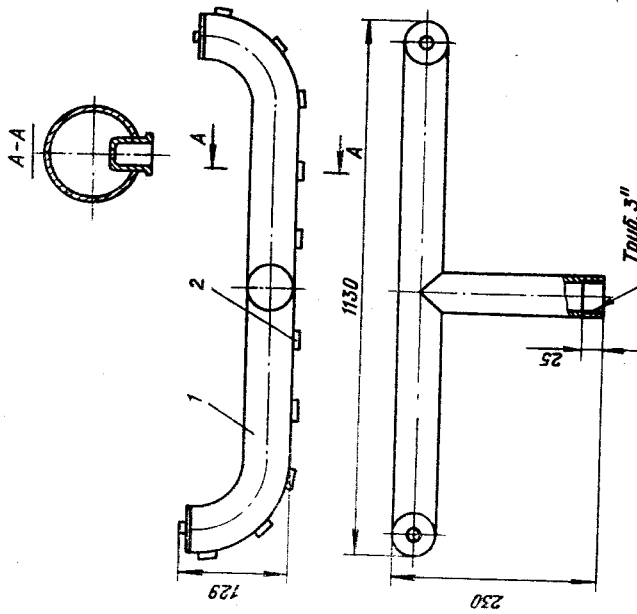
Насадок дуговой шнековый РДШ-М (черт. С761.000, ВНИИПО):
